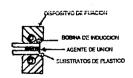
Soldadura electromagnética. (Ref. 2).
